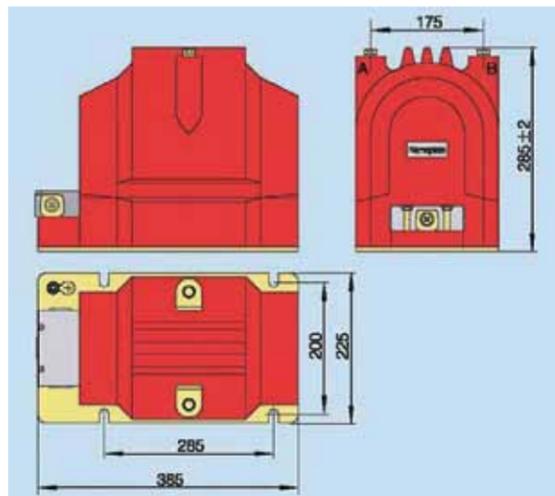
Внешний вид и размеры трансформатора напряжения JDZW-10
